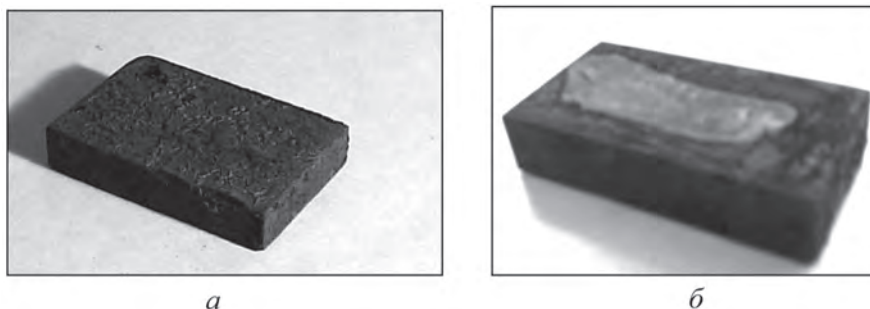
Модельный образец ножа ФТИ 5.001.1677 (40×30×15): а – образец из стали 6ХВ2С; б – образец из стали У8А после ТО
